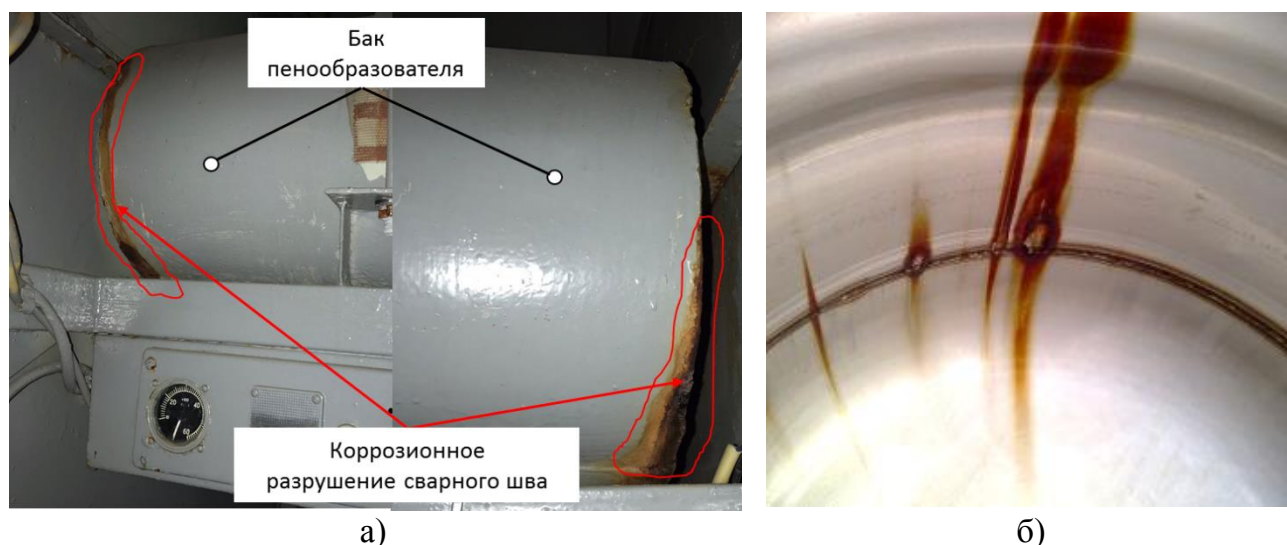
Коррозия сварных швов бака пенообразователя автоцистерны пожарной ЗИЛ АЦ 3.2-40: а- коррозия сварных швов бака пенообразователя снаружи; б - коррозия сварных швов бака пенообразователя автоцистерны пожарной (вид внутри)
